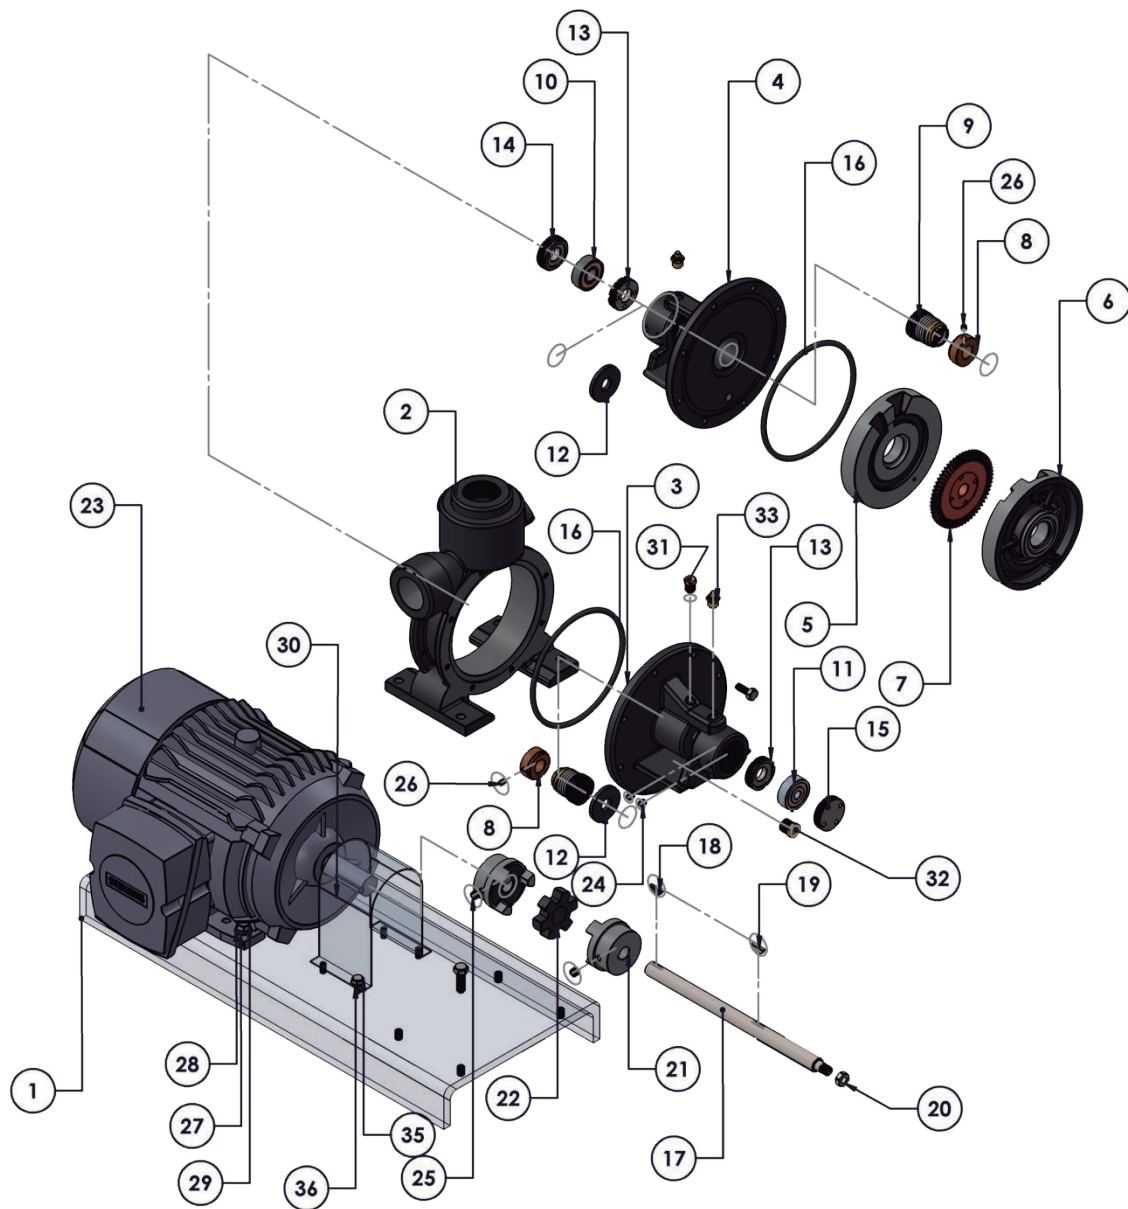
Vista del explosivo de la bomba (Sello mecánico)
